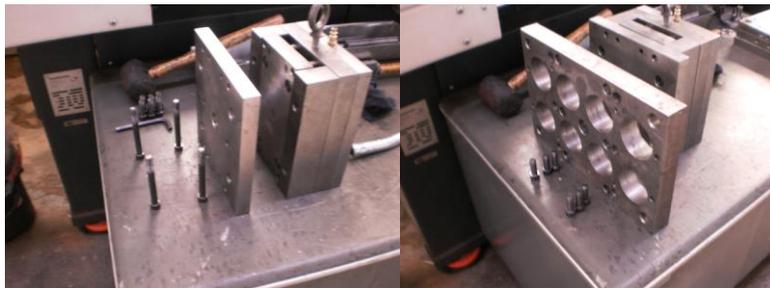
Placas de portamolde con tornillos de ensamble (izq.) y placa aumento para ajustar dimensiones a máquina (der)
